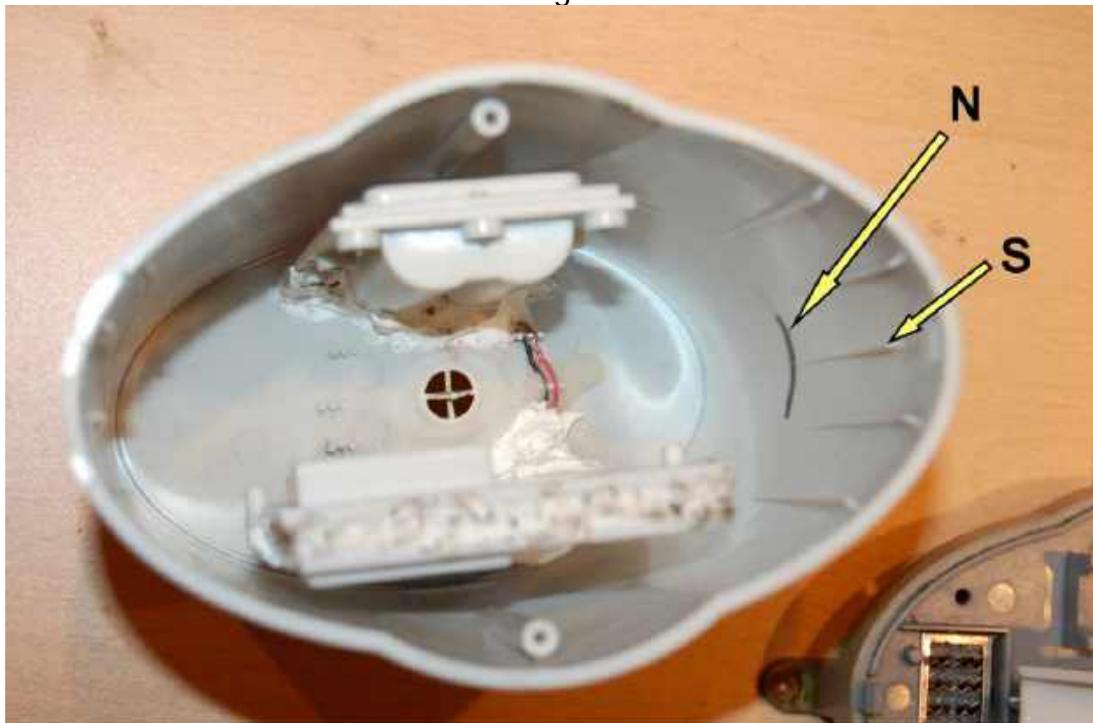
, Blick auf die Grundplatte des Regenmessers
